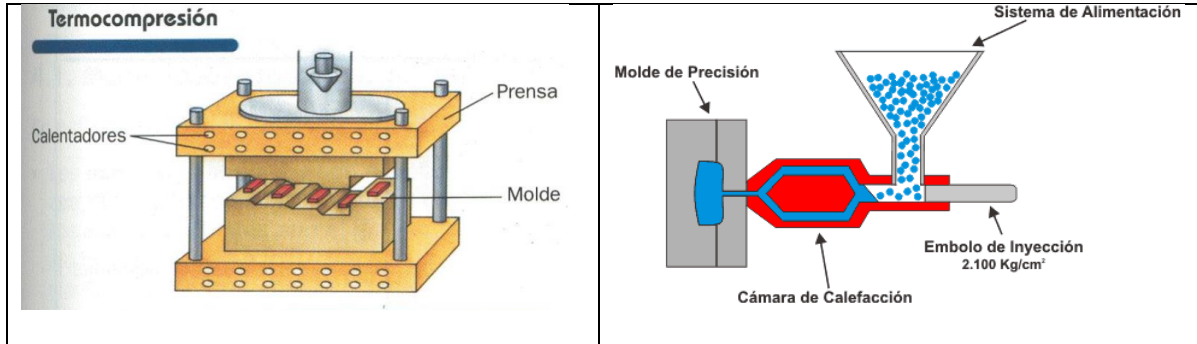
Izqda: Técnica de termocompresión. Drcha: Moldeo por inyección [91][92]
